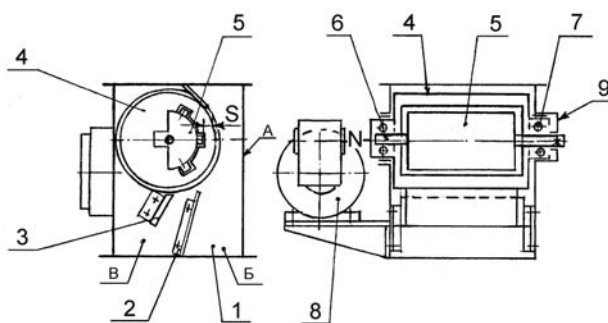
Магнитный сепаратор. 1 – корпус, 2 – перегородка, 3 – скребки, 4 – барабан, 5 – магнитная система, 6, 7 – опоры, 8 – привод.
